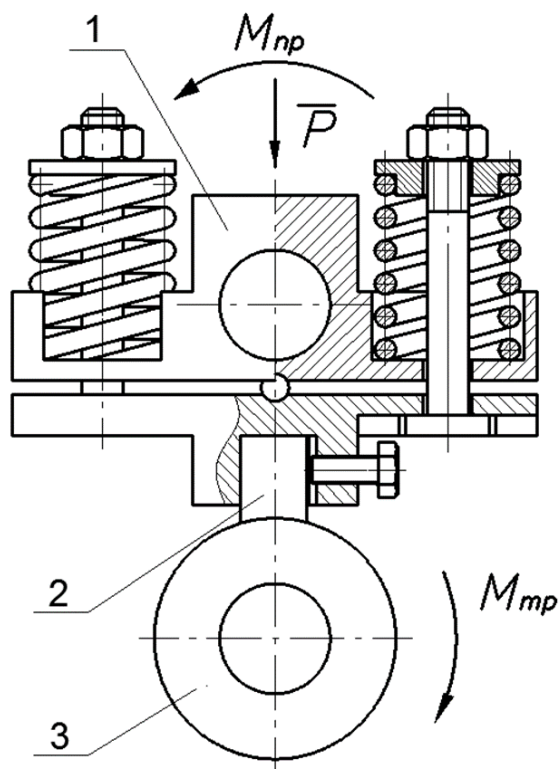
Самоустанавливающееся приспособление для крепления образца (колодки) на машине трения СМЦ-2
